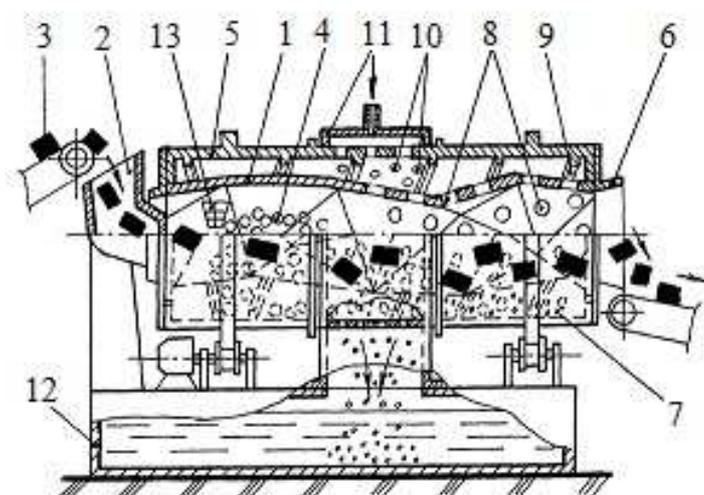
Станок для непрерывной отделочно-зачистной и упрочняющей обработки деталей машин сельскохозяйственного назначения
